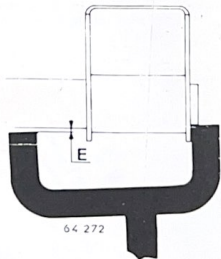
Con la pata exterior bien apoyada, la separación máxima E puede llegar hasta 2 mm.
